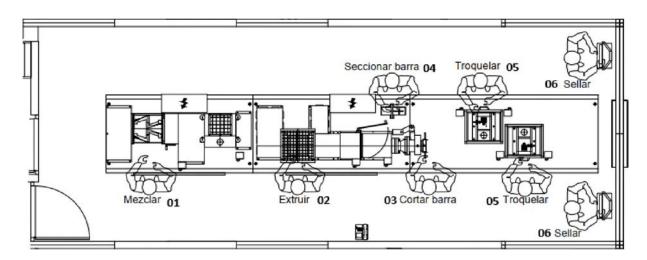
Vista en planta del proceso de manufactura de semisólidos.
